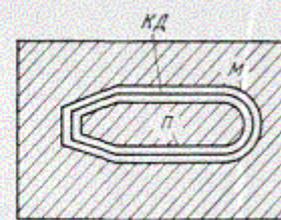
Внешние контуры режущих кромок пуансона *П* и матрицы *М*; *КД* – кромка обрабатываемой детали
